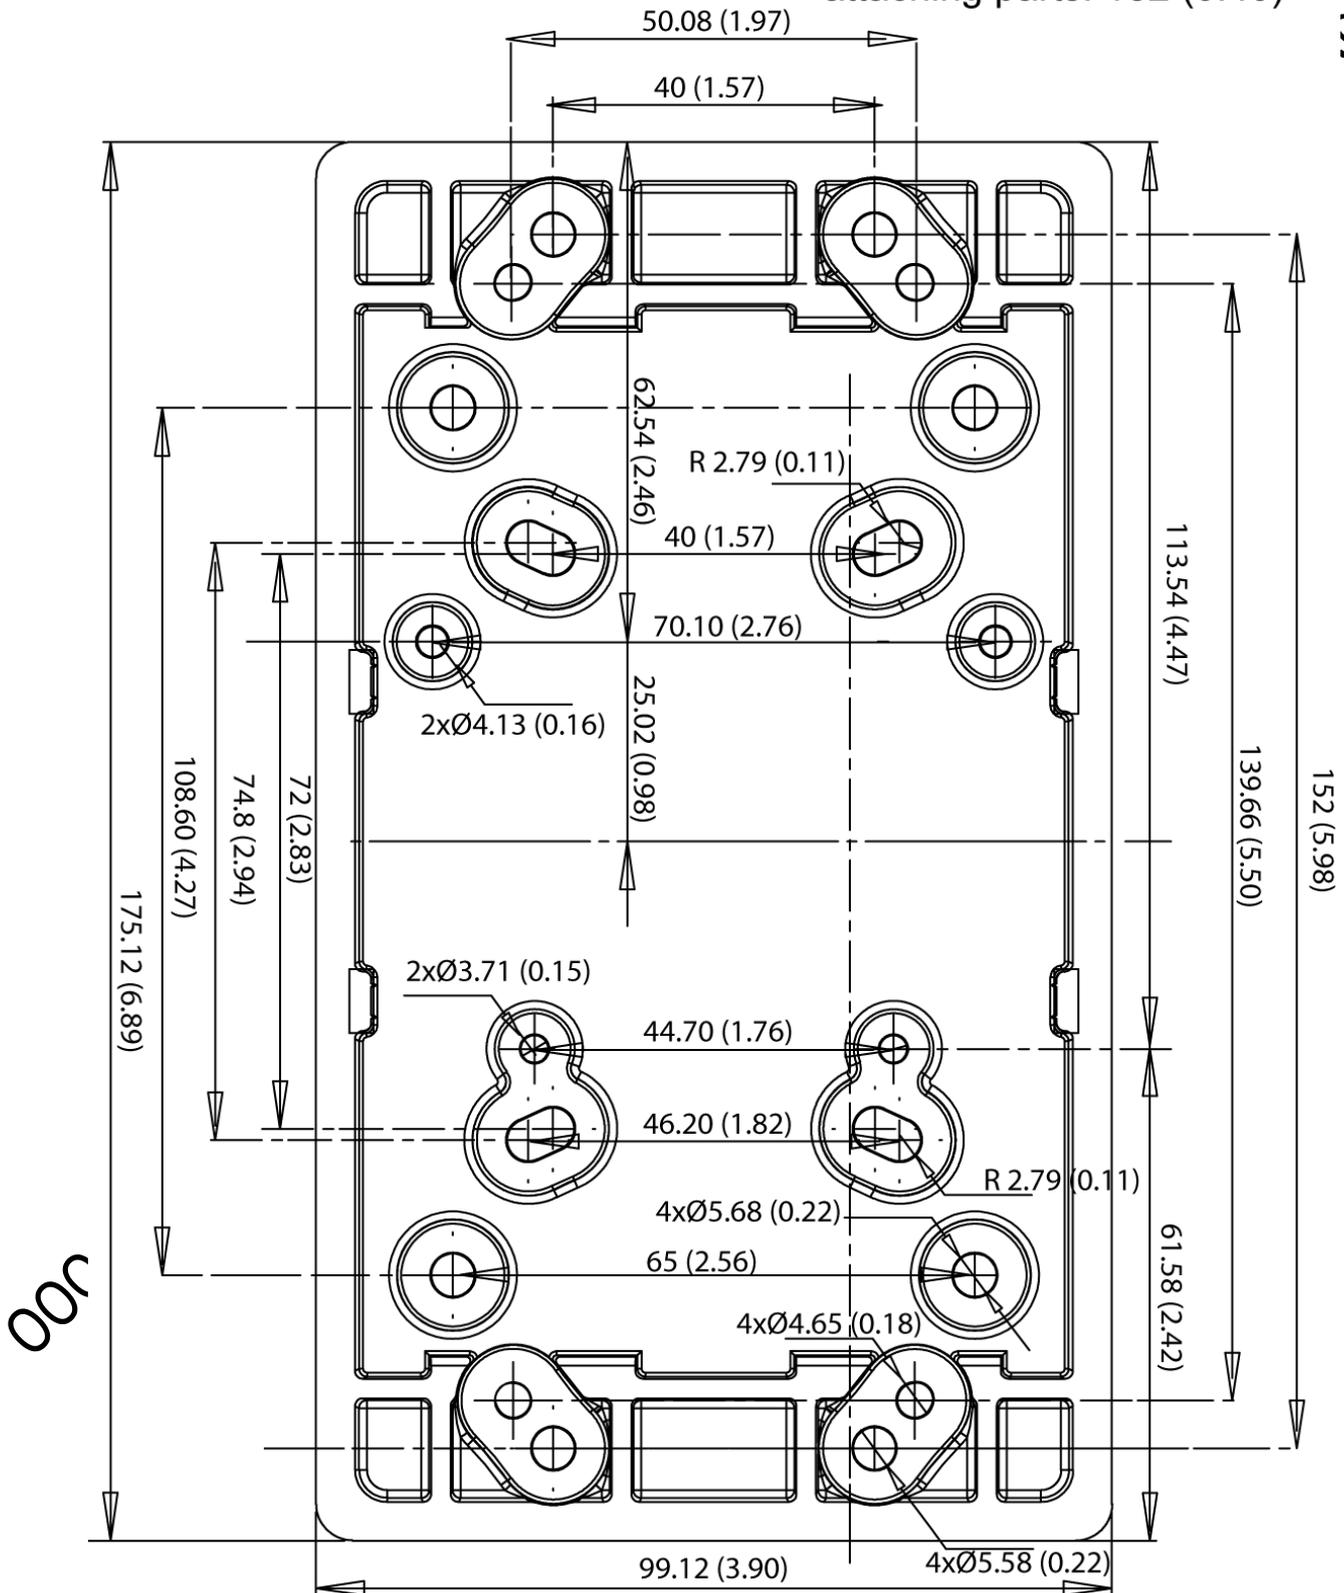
Внешний зуммер, габаритные размеры и шаблон для сверления
